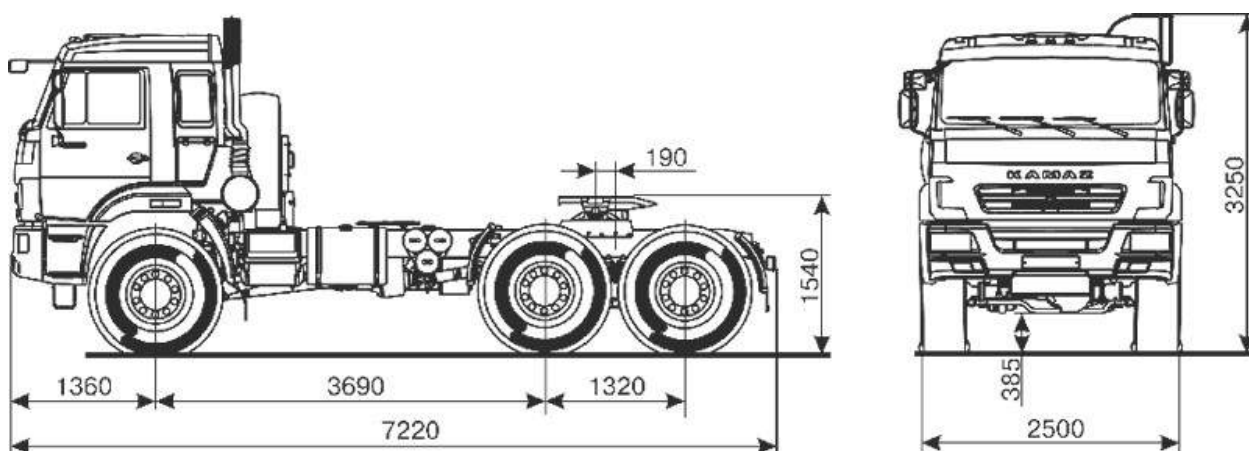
Схема основного тягача КамАЗ-44118
